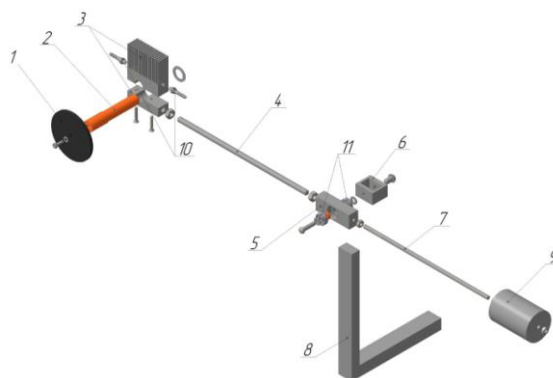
Пристрій для механізованого нанесення ЕІЛ з обертанням електроду: 1 – електрод; 2 – вісь; 3 – радіатор; 4 та 7 – штанги; 5 – корпус; 6 та 8 – деталі кріплення; 9 – противага; 10 – штуцери; 11 – підшипники
